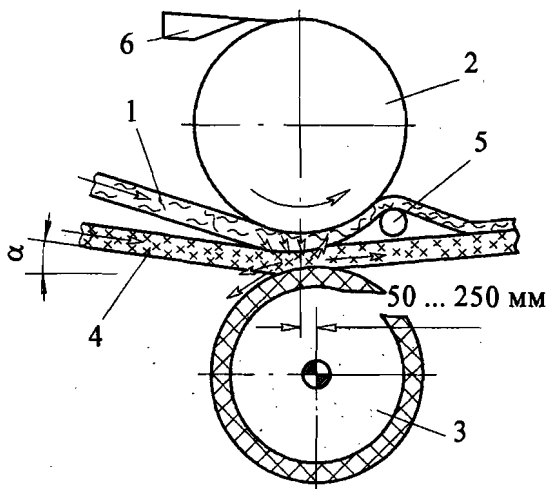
Расположение валов обычного двухвального пресса; 1 – бумажное полотно; 2 – верхний вал; 3 – нижний вал; 4 – прессовое сукно; 5 – бумаговедущий валик; 6 – шабер
